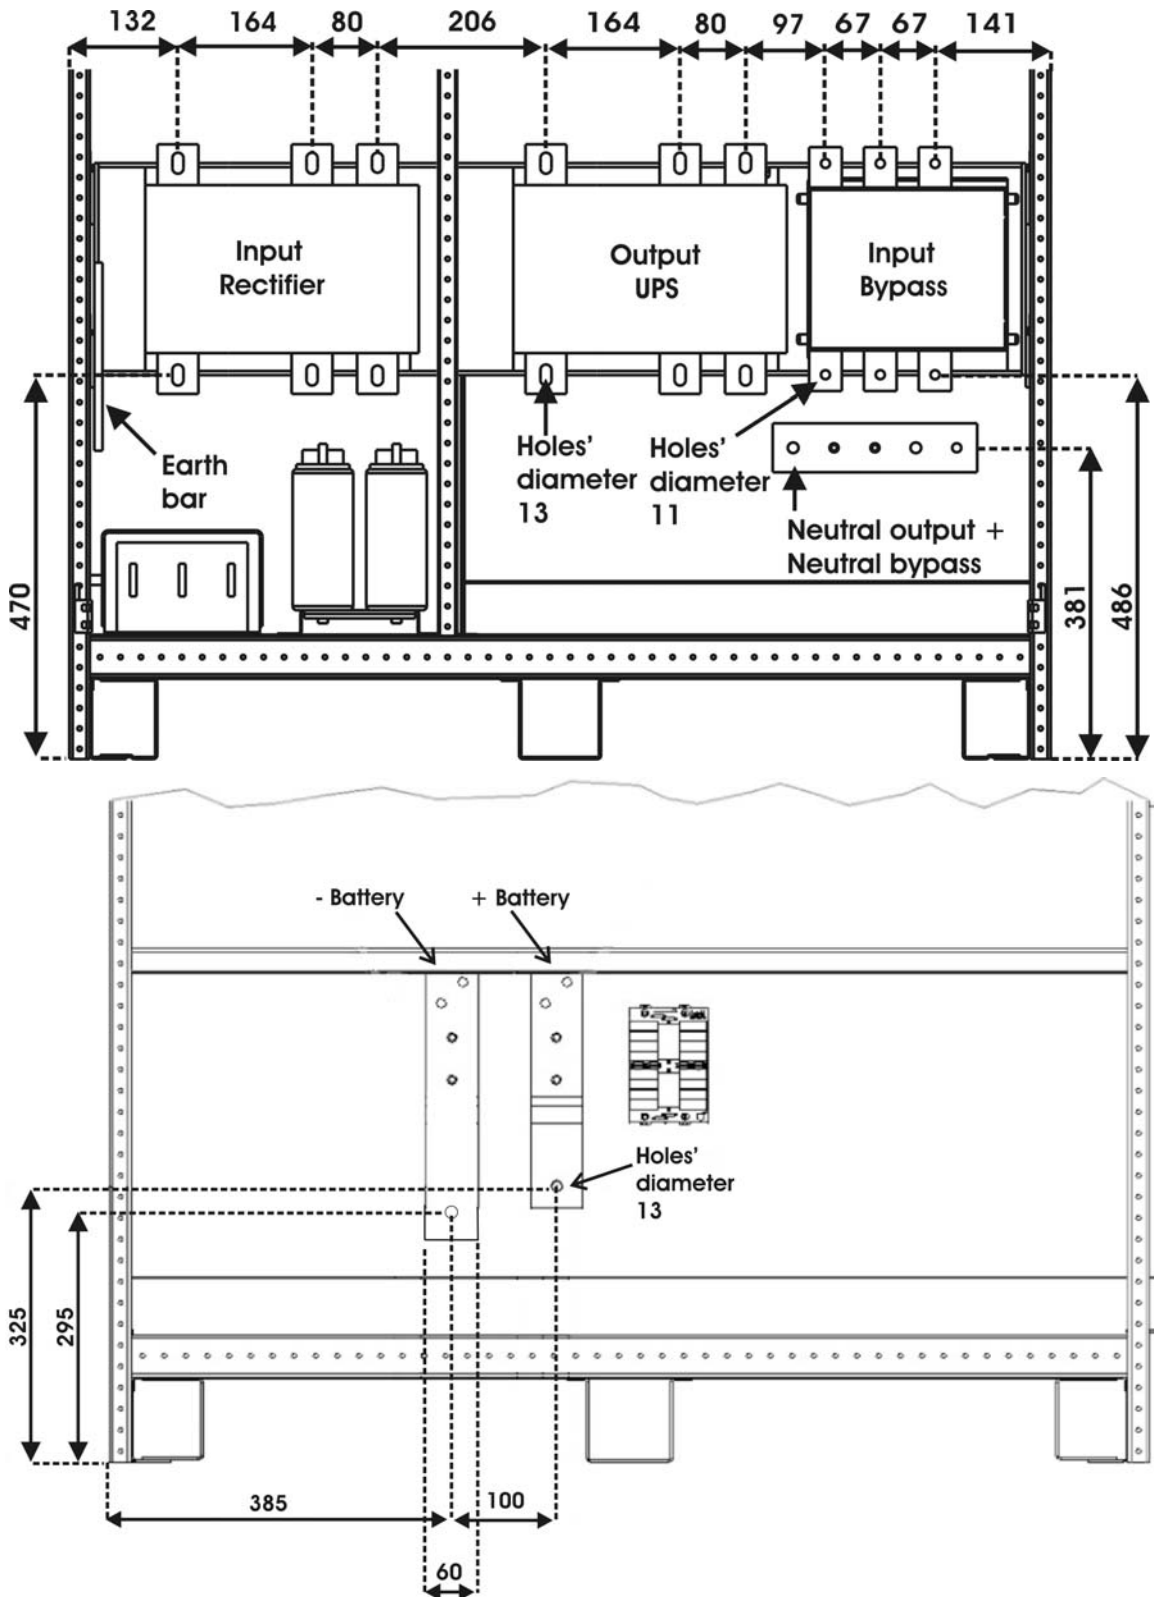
Vue de face du bornier du KEOR HP 500-600-800 kVA
